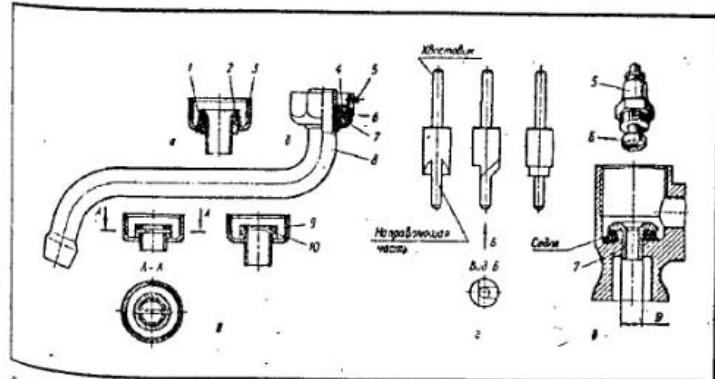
Ремонт деталей смесителя: а, б, в — изливов:
